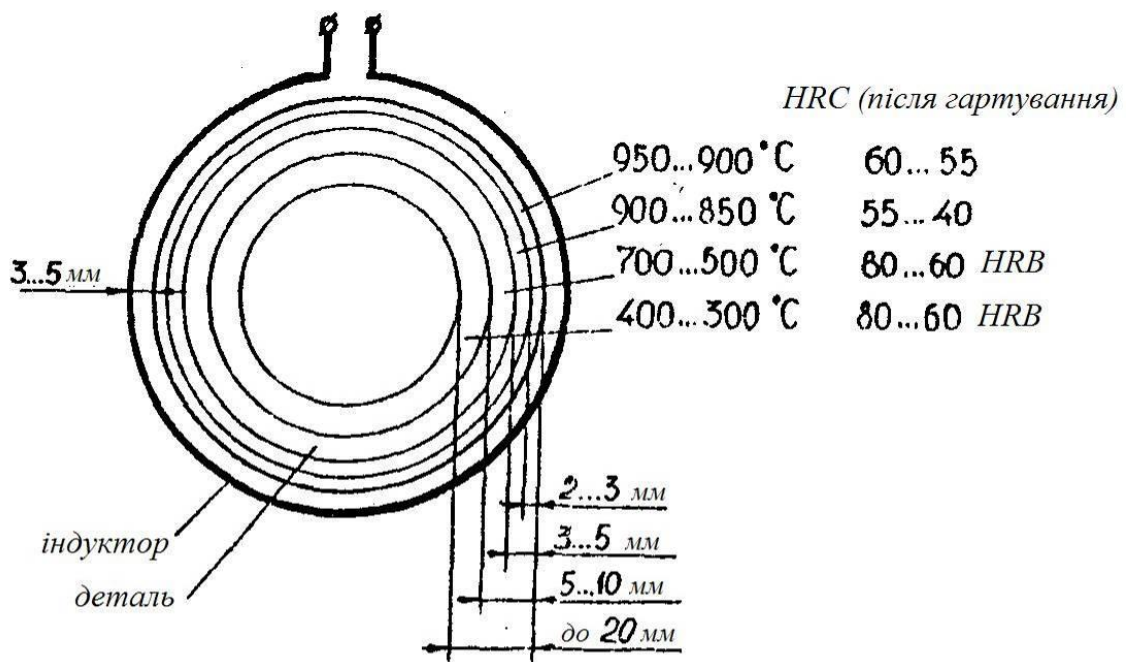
Розподіл твердості по перерізу заготовки після гартування СВЧ
